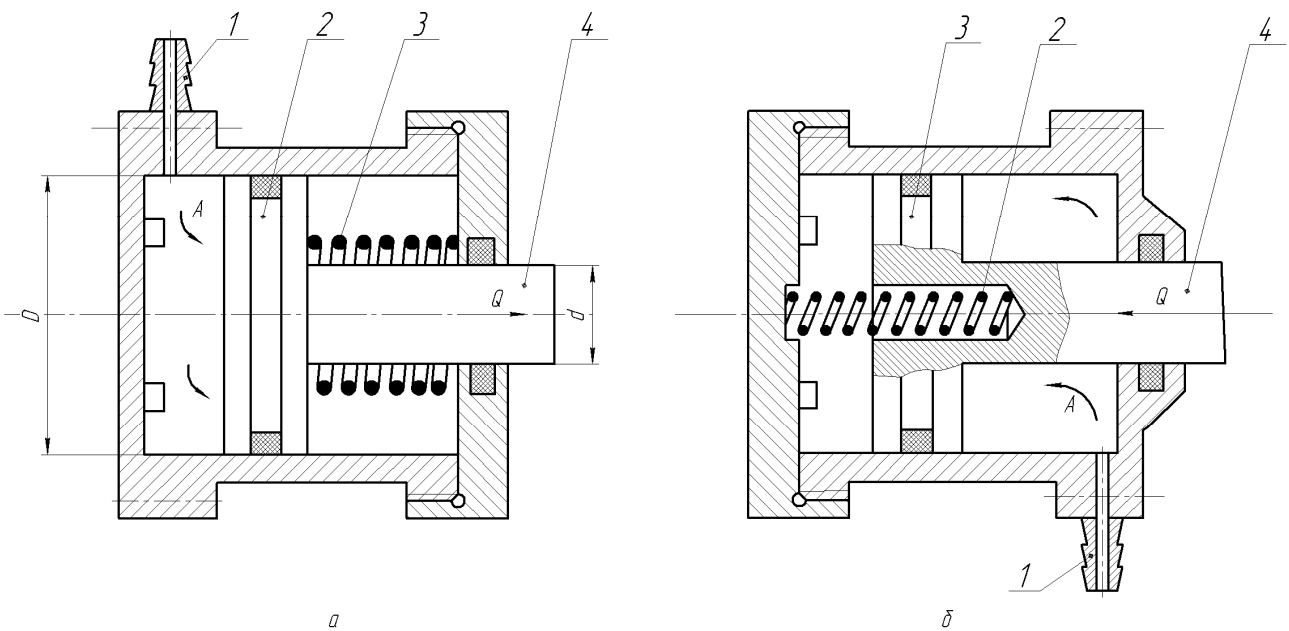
Будова й параметри різних типів гідроциліндрів одnobічної дії: a – штоухальний; b – тягнучий; 1 – штуцер; 2 – поршень; 3 – пружина; 4 – шток; A – напірна порожнина; Q – зусилля на штоку; d – діаметр штока; D – діаметр поршня
